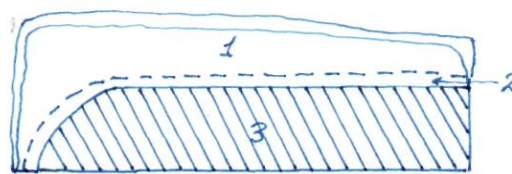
1. Полиэтиленовая пленка, 2. Шаблон, 3. Место сварки
